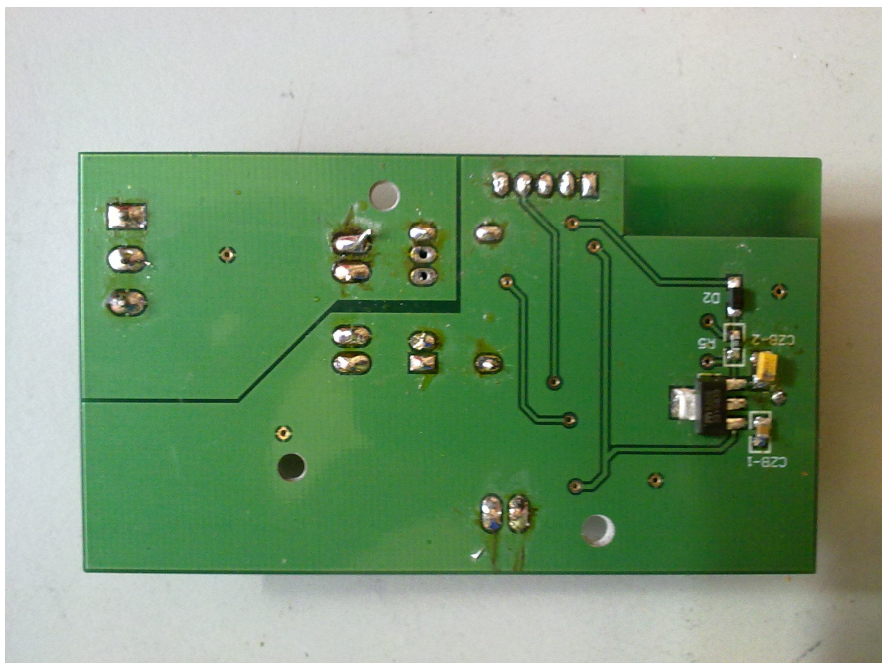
Imagen de la cara inferior del montaje final de la PCB
